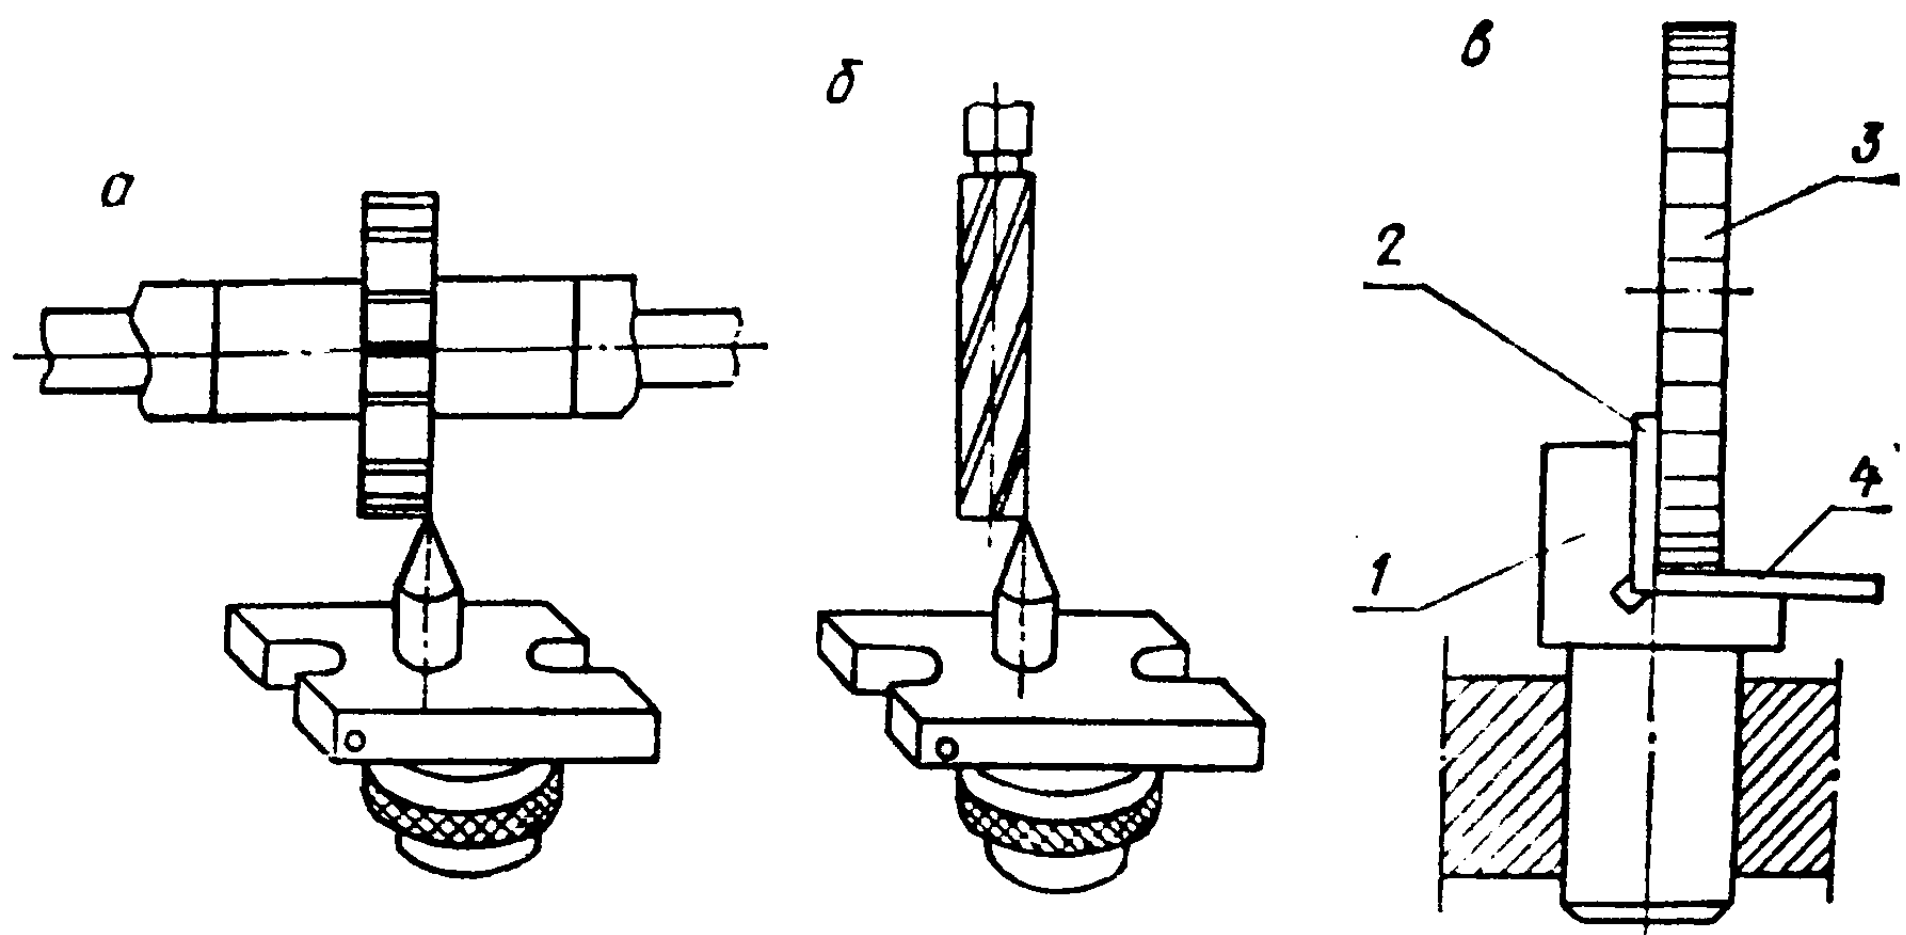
Установка фрез по центру заготовки при фрезеровании кулачковых муфт.
